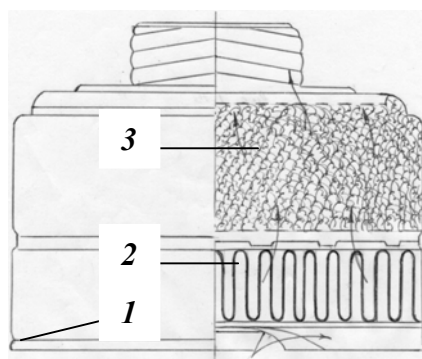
Фильтрующе-поглощающая коробка малого габарита:
